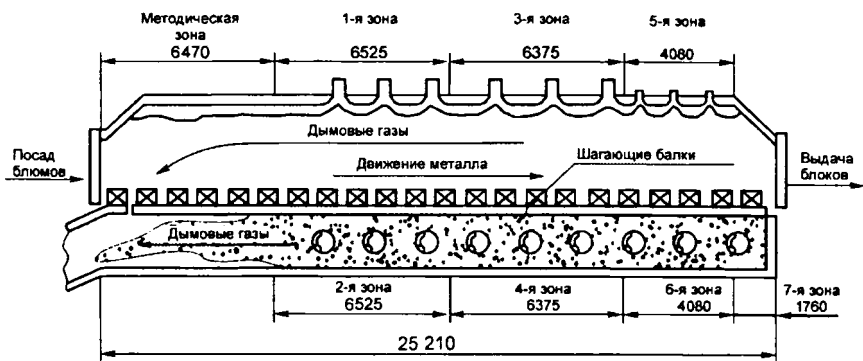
Схема нагревательной печи с шагающими балками стана 850
